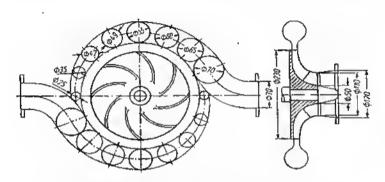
Bosquejo de la unided hidráulica de una bomba
